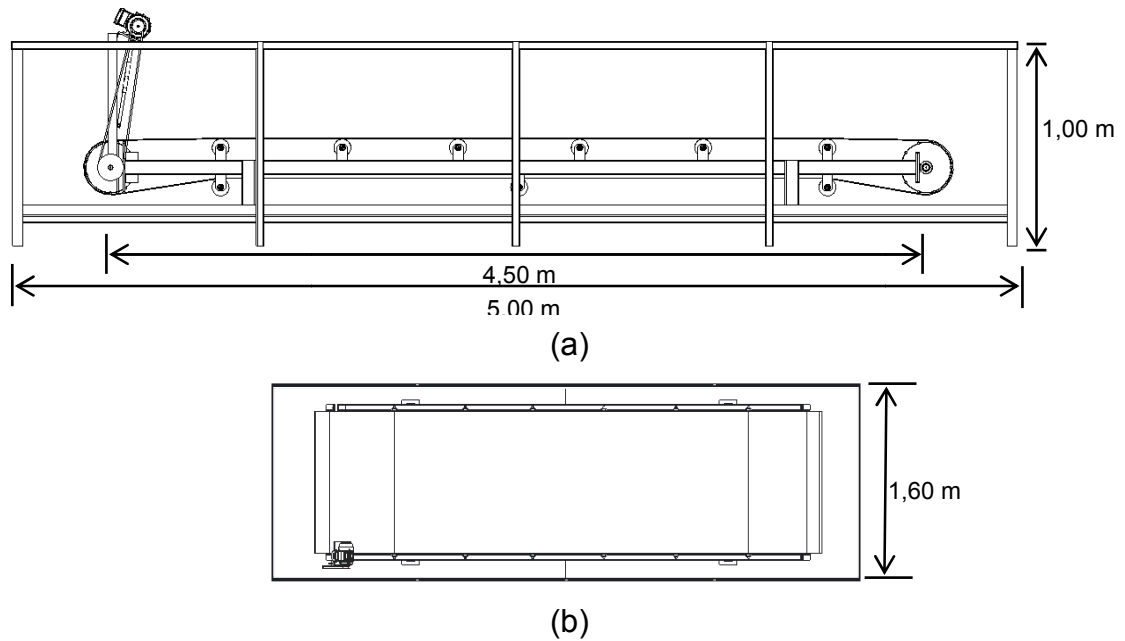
Corte longitudinal (a) e planta baixa (b) do conjunto canal hidráulico e esteira transportadora.
